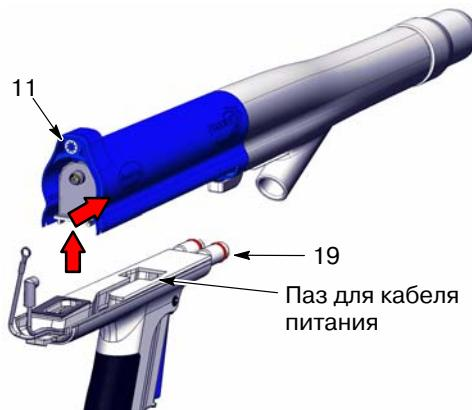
Отсоединение корпуса распылителя от рукоятки
